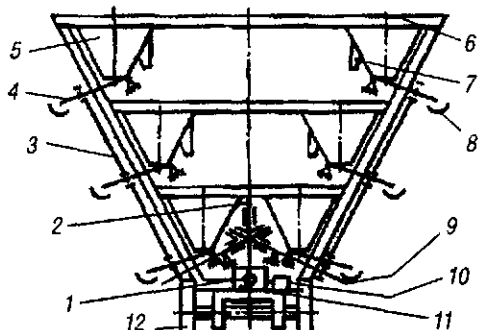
Схема вибрационного раздатчика кормов: 1 — кривошип; 2 — тяга; 3 — штанга; 4 — лоток; 5 — бункер; 6 — рама; 7 — пересыпной рукав; 8 — кормушка; 9 — двуплечий рычаг; 10 — электродвигатель; 11 — редуктор; 12 — ходовая часть
